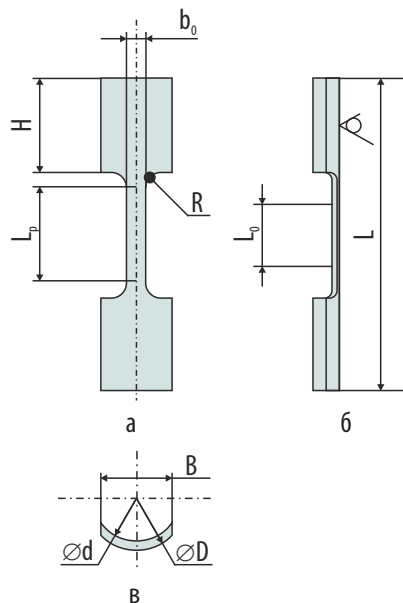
Эскиз сегментного образца для проведения механических испытаний: b — ширина рабочей части; H — высота сегмента; L_p — рабочая длина; R — радиус скругления (а); L_0 — начальная расчётная длина; L — длина образца (б); B — ширина сегмента; D , d — наружный и внутренний диаметр соответственно (в)
